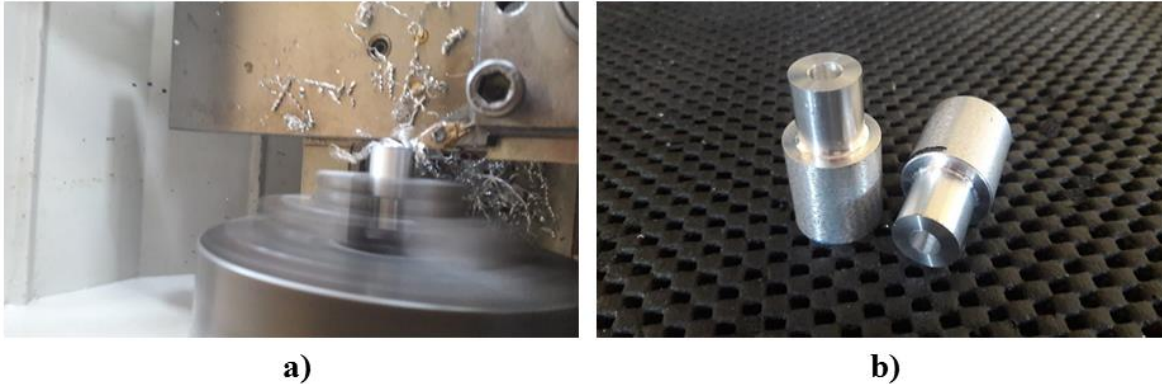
a) Generando la cabeza del tornillo, b) Cabezas de los tornillos.
